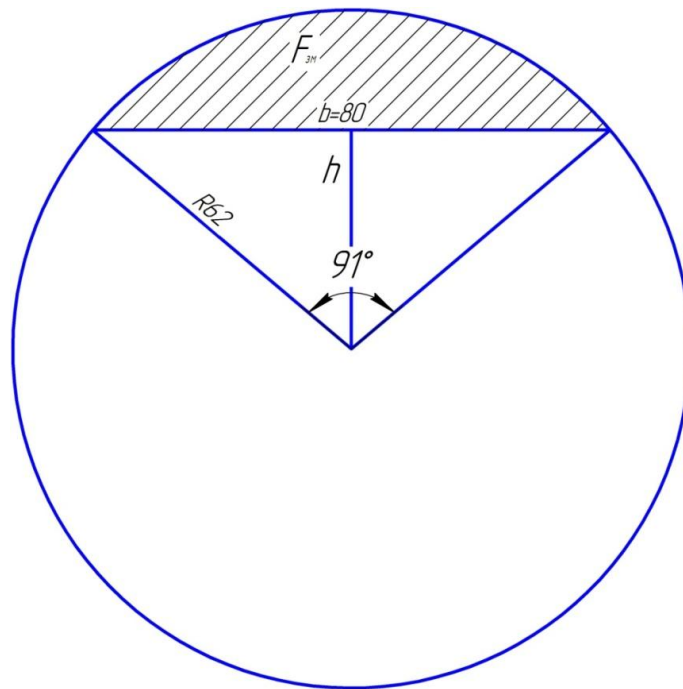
Визначення площі поперечного перерізу напівтрубки.
